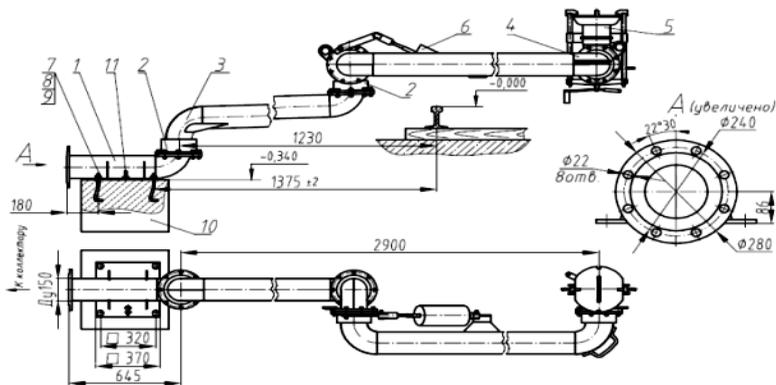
Устройство УСН: 1 – патрубок опорный; 2 – шарнир; 3, 4 – труба; 5 – присоединительная головка; 6 – компенсатор; 7 – болт фундаментный; 8 – гайка; 9 – шайба; 10 – фундамент; 11 – болт заземления
